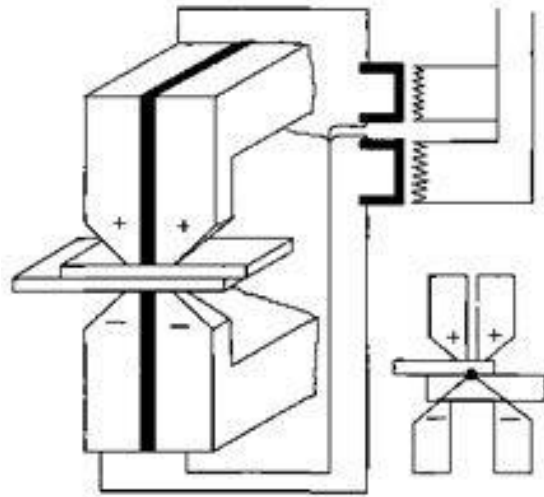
Схема перехресного точкового зварювання Тейлора
